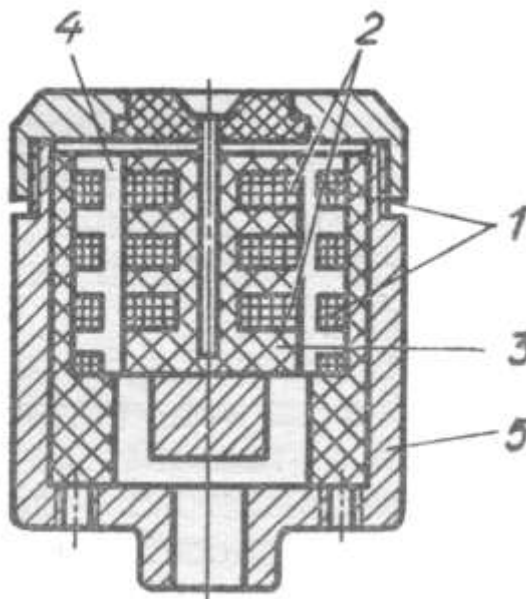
Прохідний ВСП для контролю якості термічного оброблення швацьких головок: 1 – збуджувальна навитка; 2 – вимірювальна навитка; 3, 4 – каркаси; 5 – корпус
